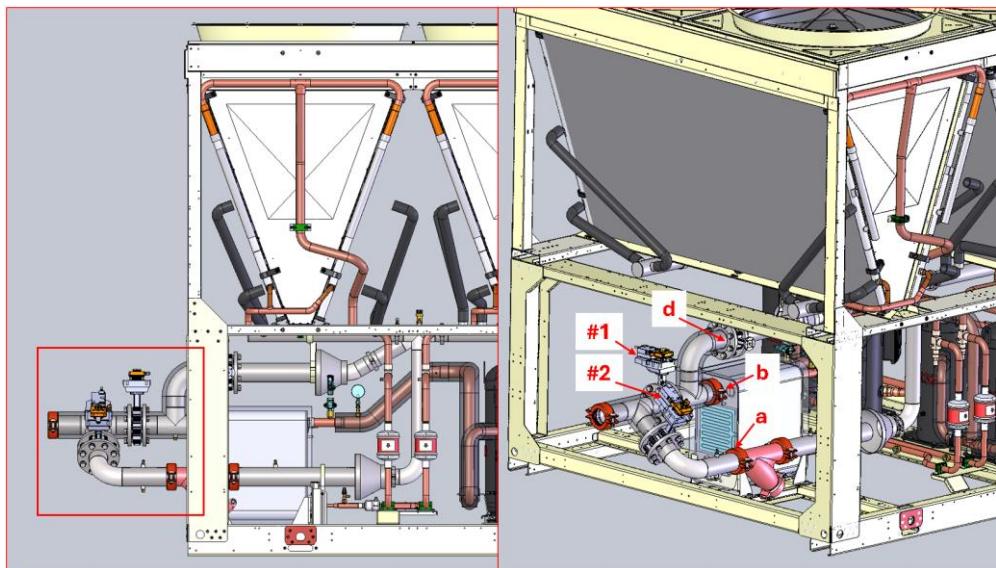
Potrubí mimo půdorys volně chlazených jednotek.
